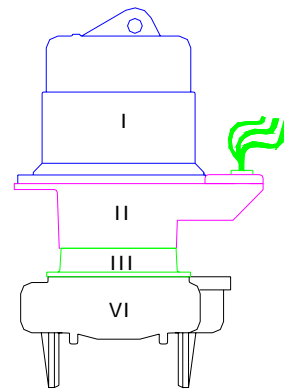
↑ Elementos principales de una bomba ROBUSTA accionada con un motor FRAME 180.
